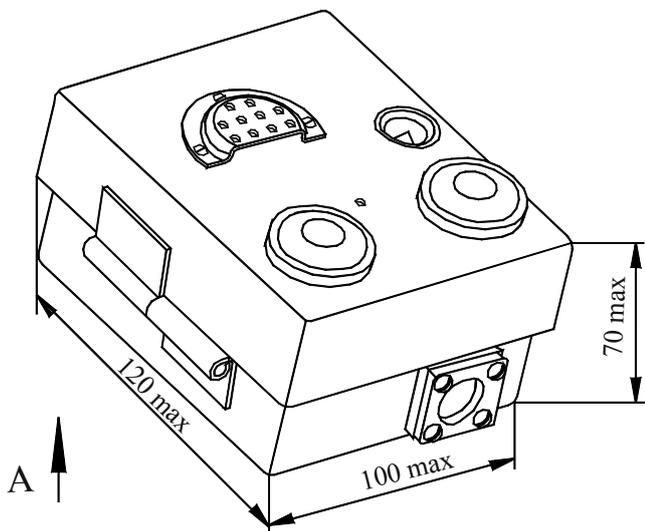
Внешний вид и габаритные размеры ПУ.У
